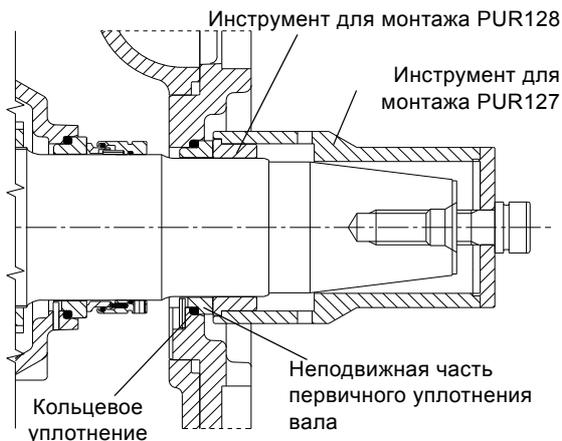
Установка неподвижной части первичного уплотнения вала, типоразмер 74
